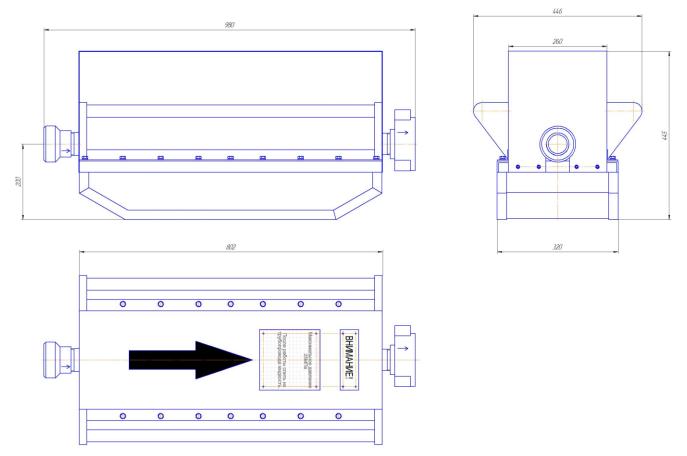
Внешний вид и габаритные размеры СКПЖ-1(.1).
